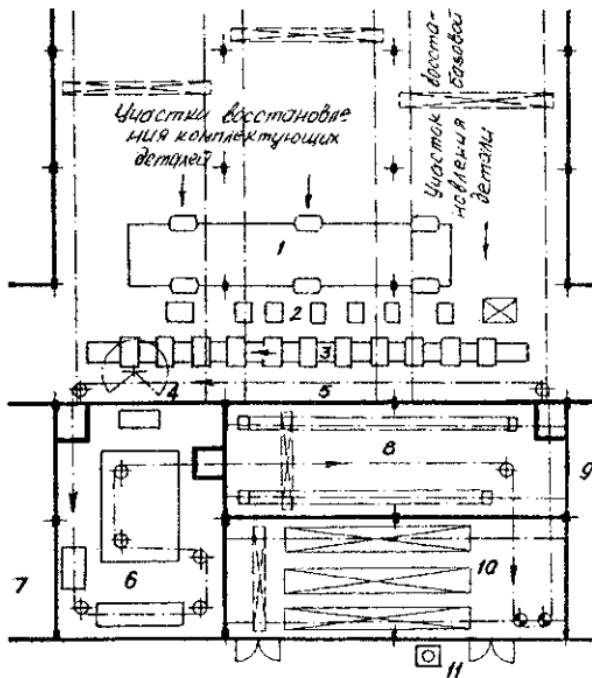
Схема расположения участков комплектования деталей, сборки, окрашивания и обкатки агрегатов, обслуживающих отделений и склада сбыта:
